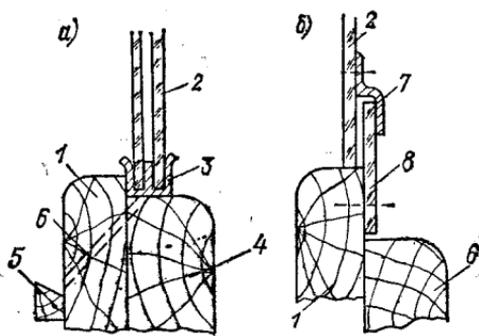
Конструкция сдвижных стекол. 1 — внутренняя накладка комингса; 2 — стекло; 3 — направляющий профиль; 4 — комингс рубки; 5 — рейка-водосборник; 6 — канал для стока воды из желобков профиля 3; 7 — направляющая планка из металла; 8 — направляющая планка из оргстекла.
